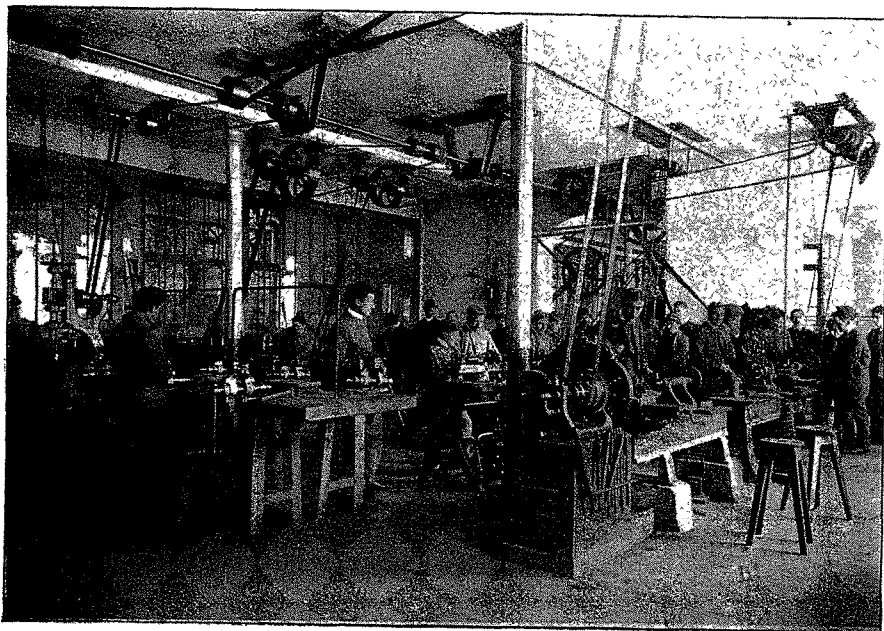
VUE DE L'ATELIER DES MACHINES-OUTILS
